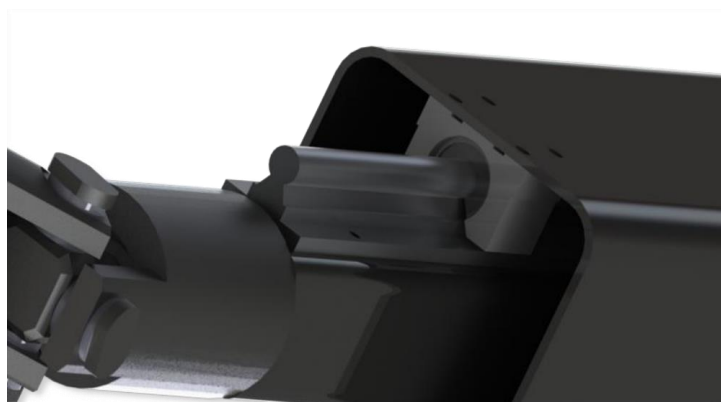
Призматический шарнир на основе линейного подшипника скольжения
